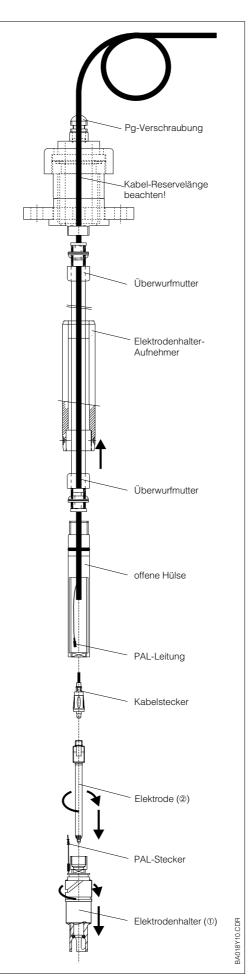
Montage pH-/Redox-Elektrode und Messkabel mit Stecker
